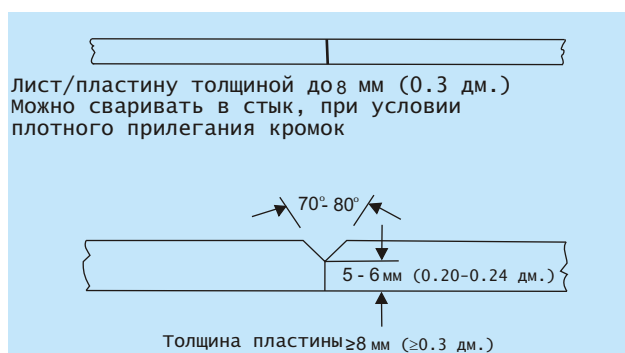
Подготовка шва для сварки плазмой и штрих-точечным методом.
